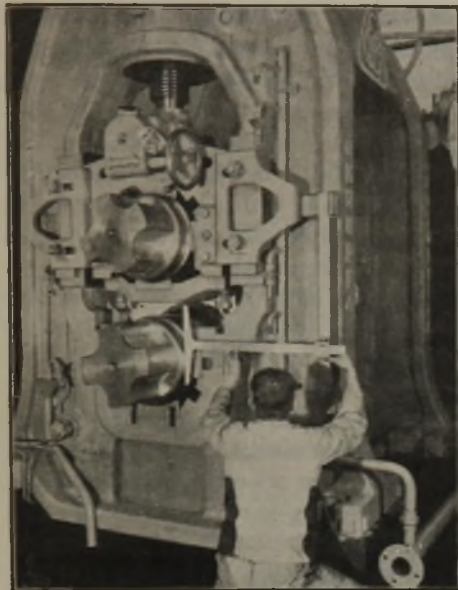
Einregeln der Walzenlage an einem Zweiwalzengerüst.
